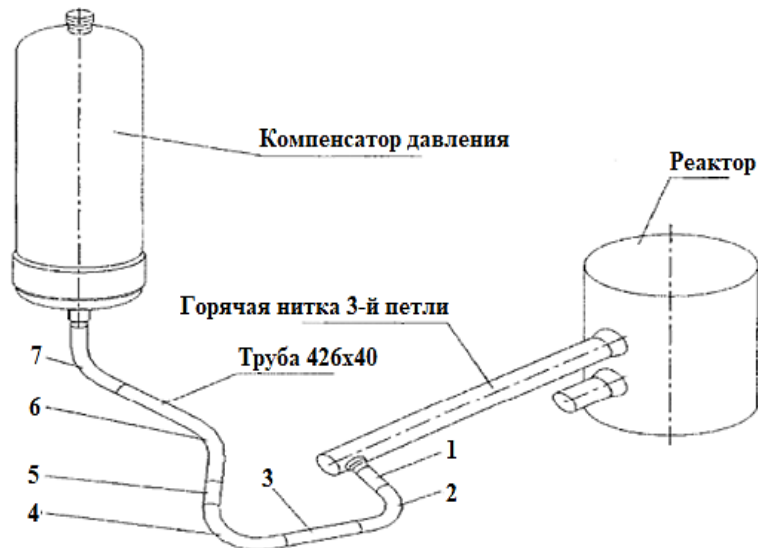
Схема соединительного трубопровода КД и горячей нитки третьей петли
